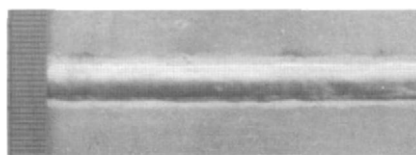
脉冲MIG焊机焊接铝合金板对接焊缝
